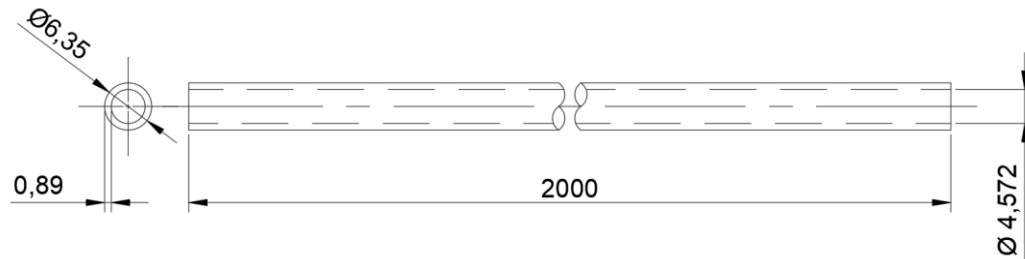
Dimensiones del intercambiador de calor tipo tubo recto
